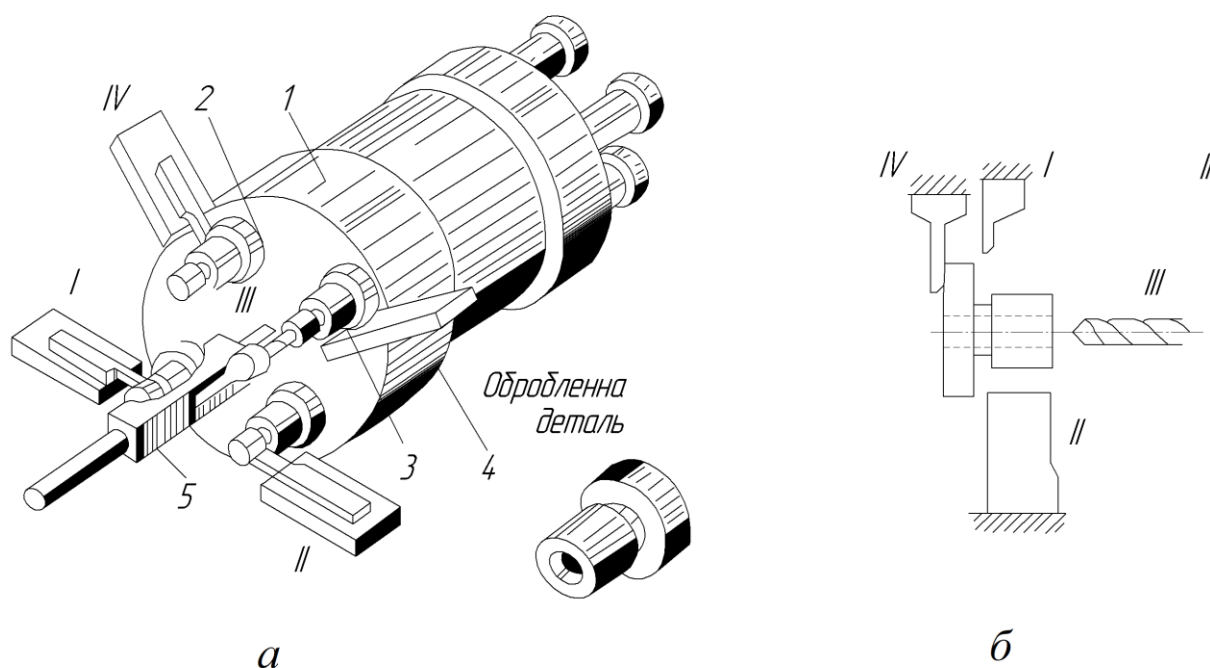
Схема обробки деталі на багатошпиндельному напівавтоматі
